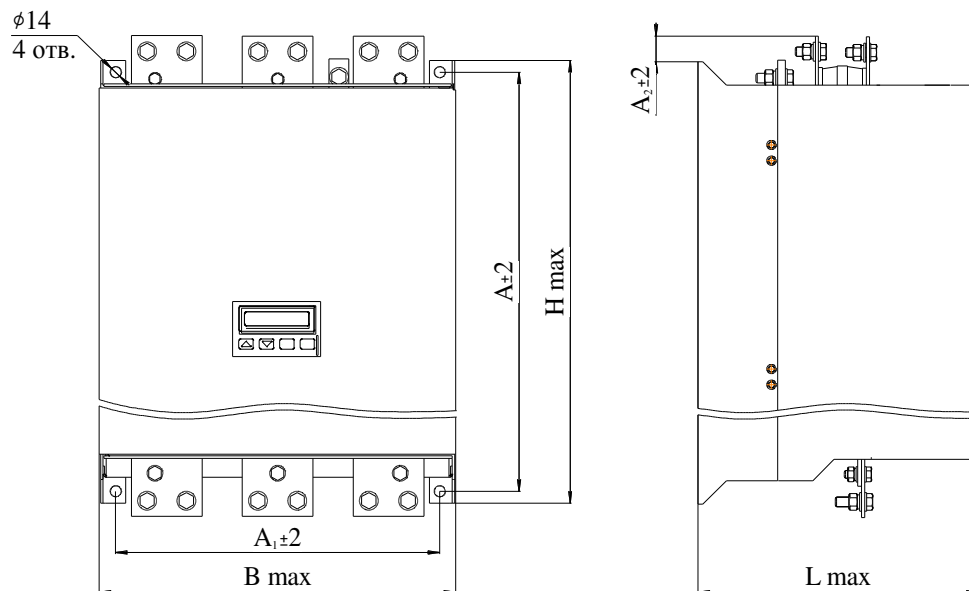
в - Габаритные и установочные размеры УПП1-Х7ХП
